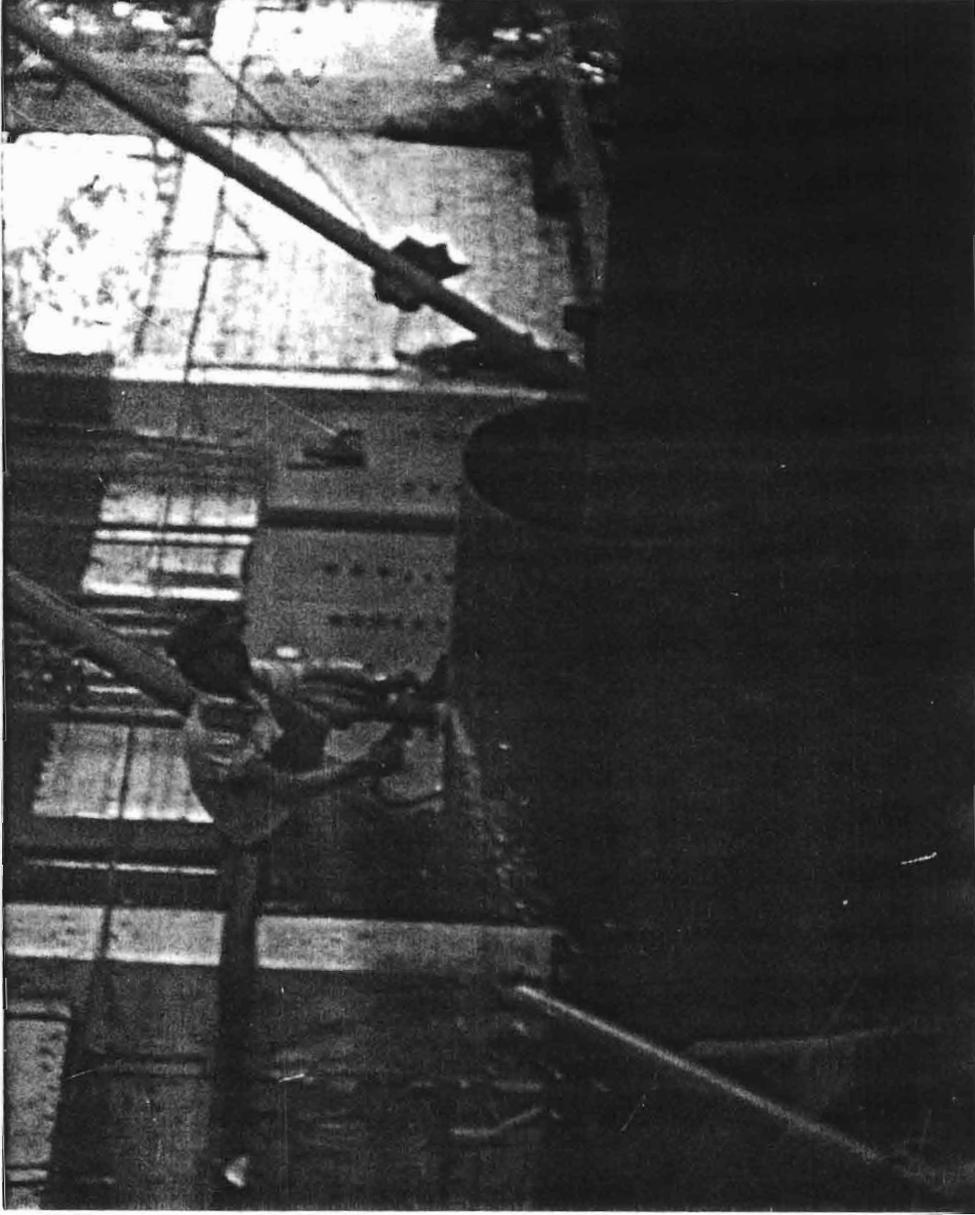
ELABORACION DE PUNTOS DE SOLDADURA EN TUBOS METALICOS
